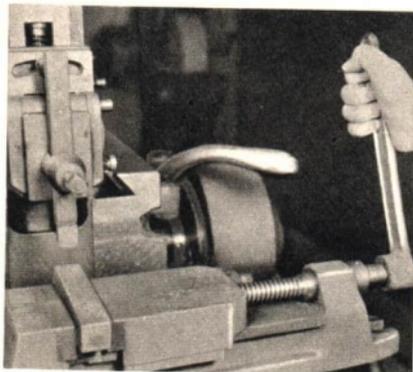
/3. Schraubspindel an einem Maschinenschraubstock
